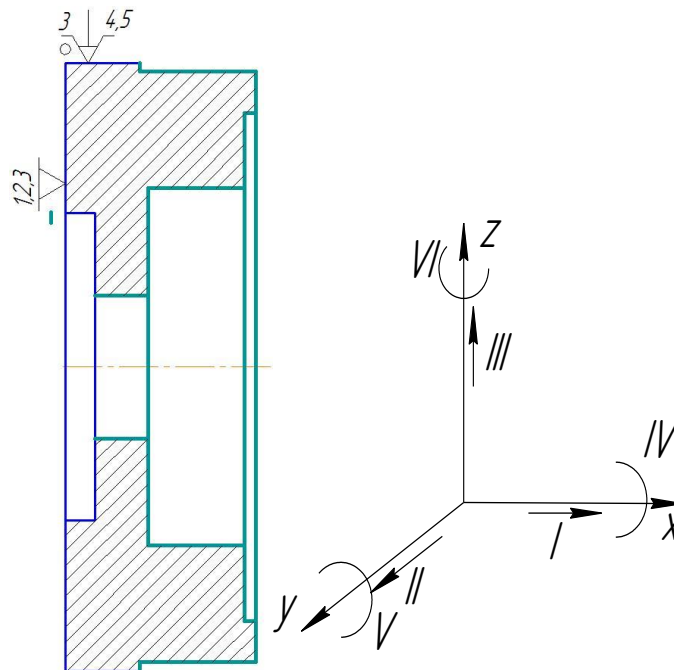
Схема базування заготовки на токарній з ЧПУ операції
